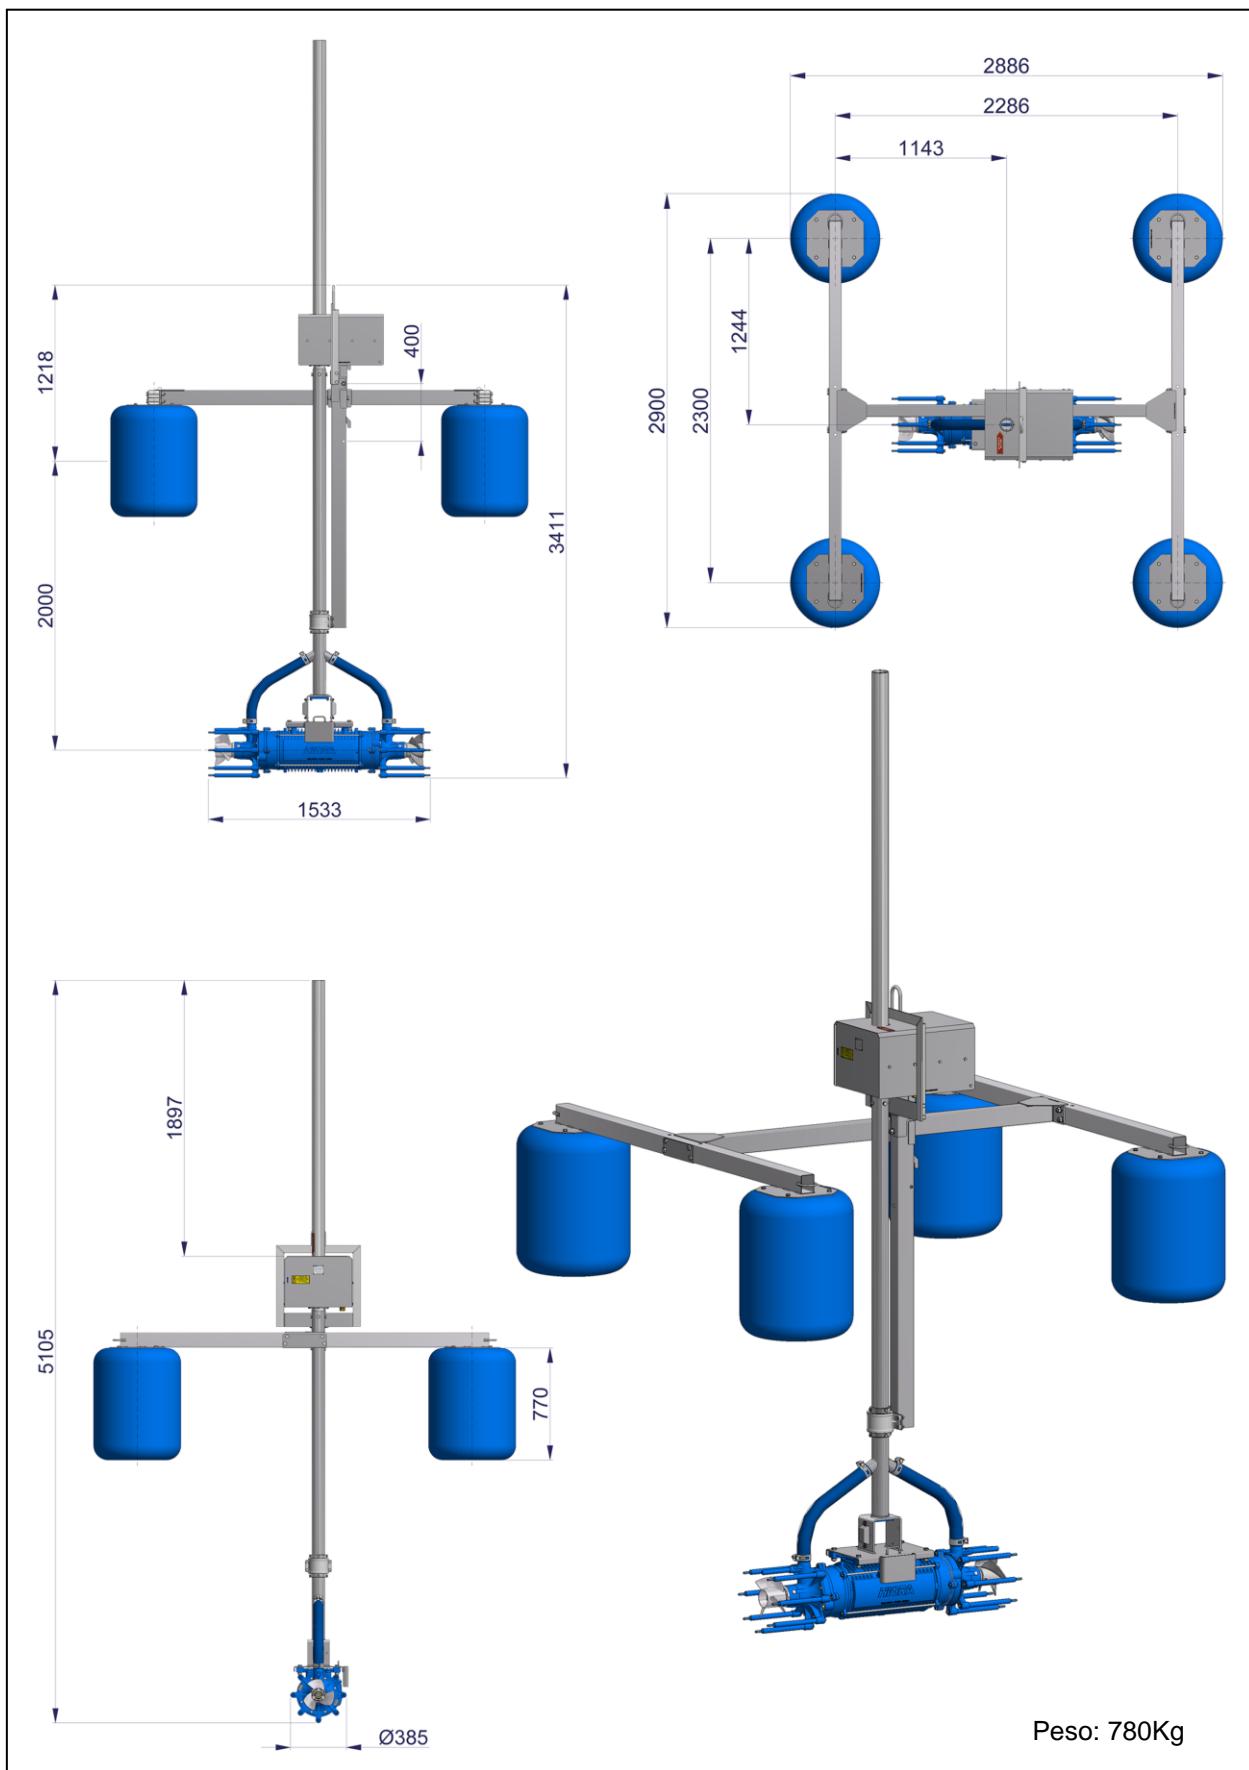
Dimensional TORNADO-R BITURBO 50,60 e 80CV
